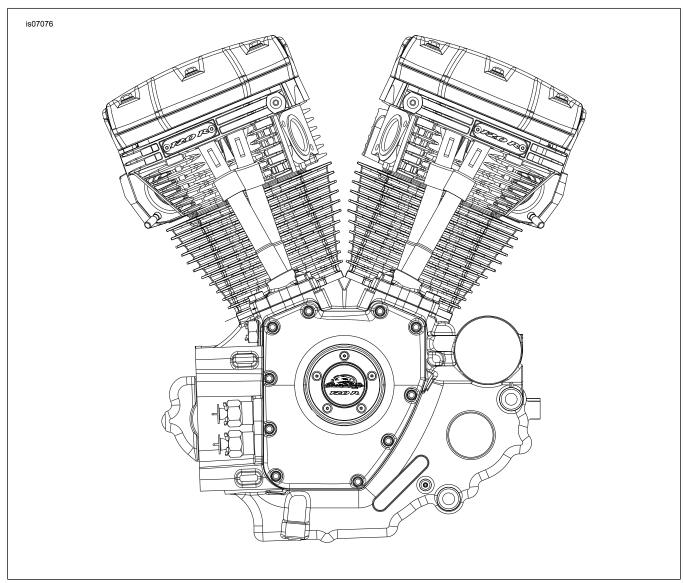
Pièces de rechange : Ensemble moteur, SE 120R complet
